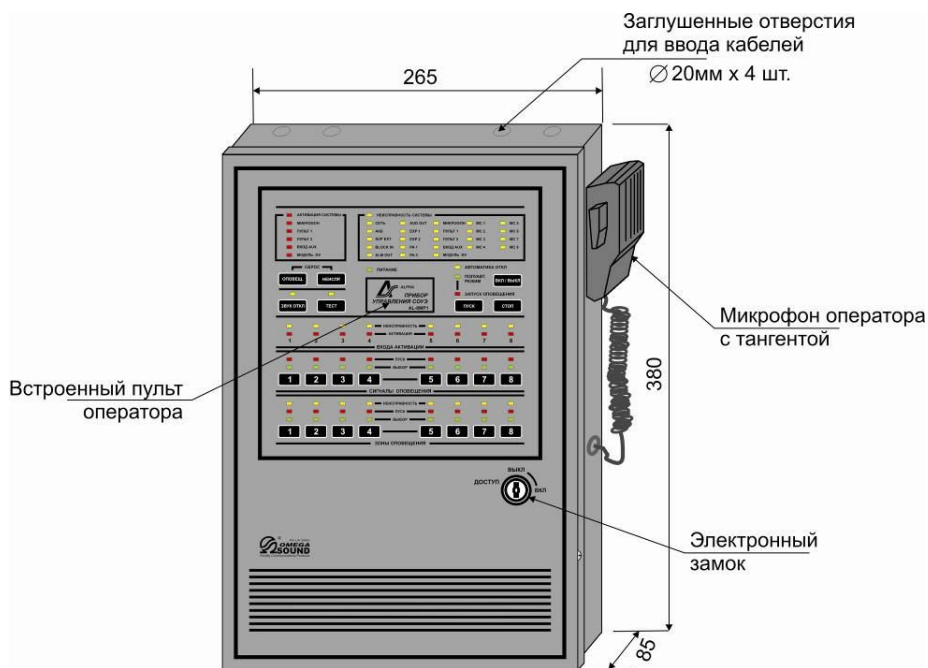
Внешний вид и габаритные размеры ППУ AL-8MP1
